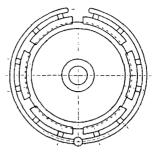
大尺寸轮形铸件两箱造型工艺(湿型)
